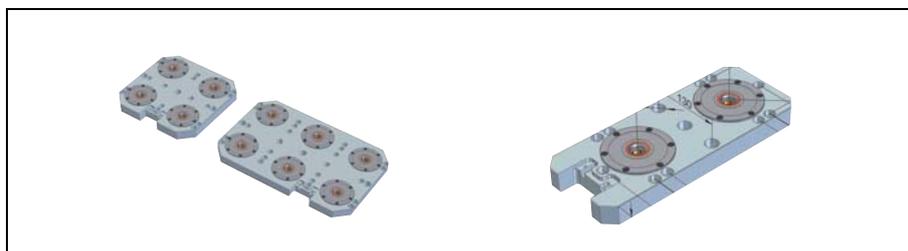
Стандартная система базирования для вертикально-фрезерных станков
